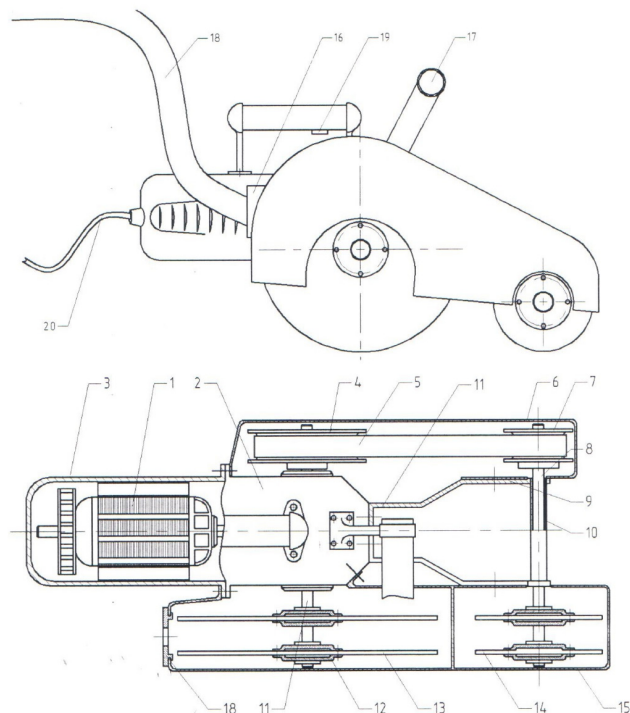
1 – электродвигатель; 2 – конический редуктор; 3 – корпус штробореза; 4 – шпиндель; 5 – клиновой ремень; 6 – кожух ременной передачи; 7 – ведомый шкив; 8 – ведомый вал направляющий фрез; 9 – кронштейн крепления ведомого вала; 10 – втулка; 11 – шпиндель; 12 – фиксаторы (крепления) главных фрез; 13 – главная фреза; 14 – направляющая фреза; 15 – кожух защитный; 16 – фитинг для промышленного пылесоса; 17 – рукоятка; 18 – кнопка пуска; 19 – шланг промышленного пылесоса; 20 – электрический кабель
